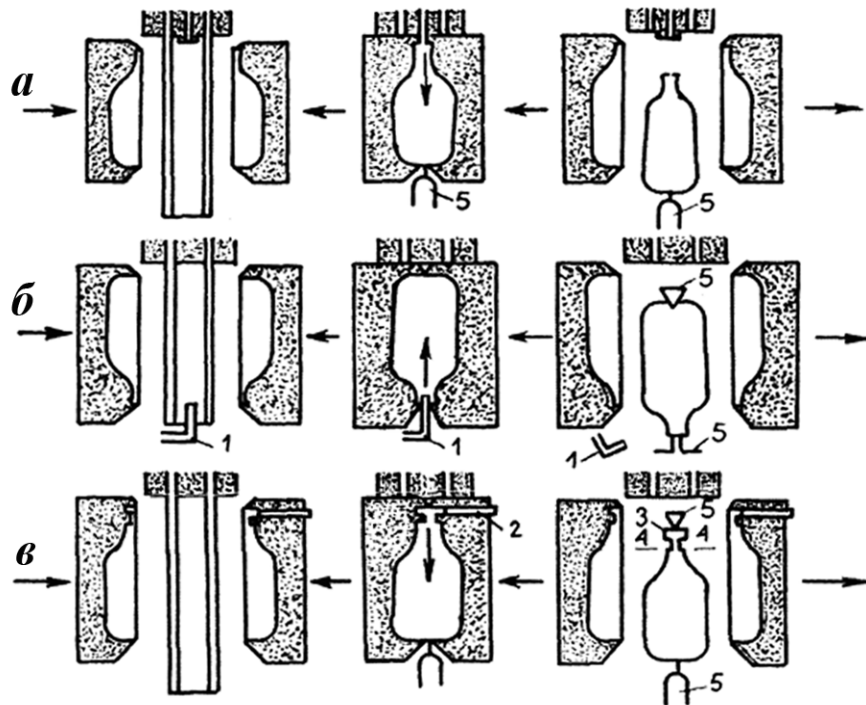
Способи роздуву заготовки: а – через дорн; б – через ніпель; в – через голку;
